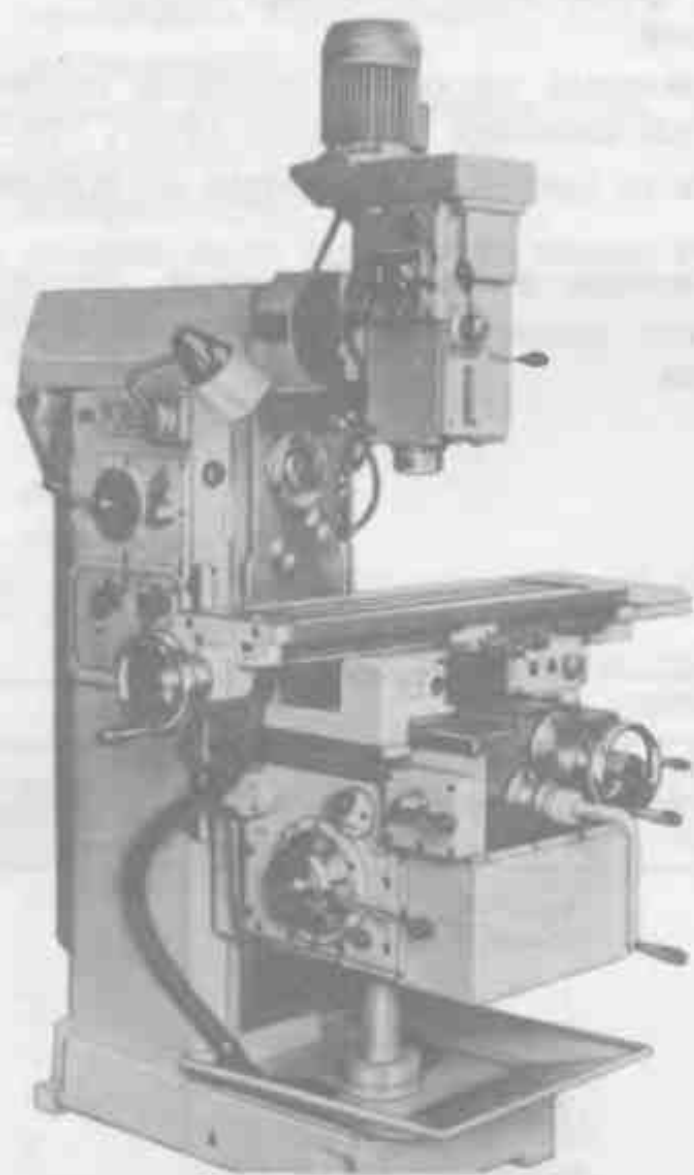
Станок горизонтально-фрезерный консольный с вертикальным поворотным шпинделем 6Т80Ш
